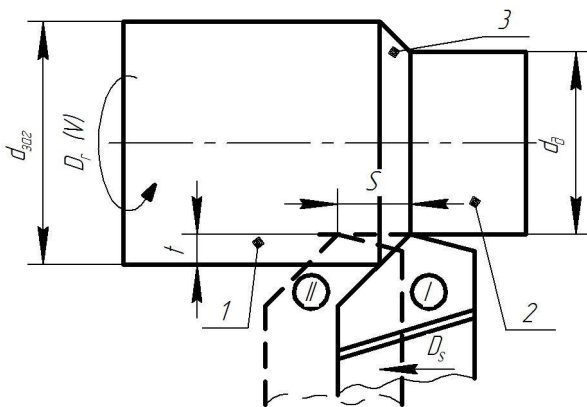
Поверхні обробки: 1 – оброблювана; 2 – оброблена; 3 – поверхня різання
